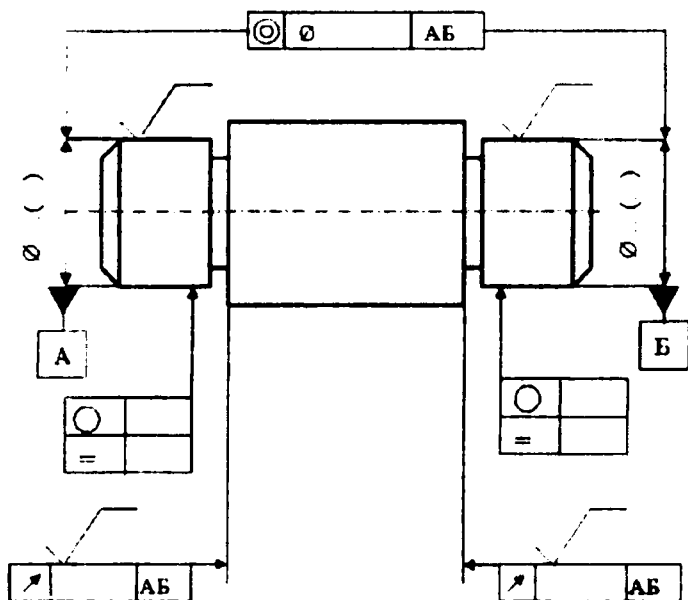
Обозначение допусков на рабочем чертеже вала
